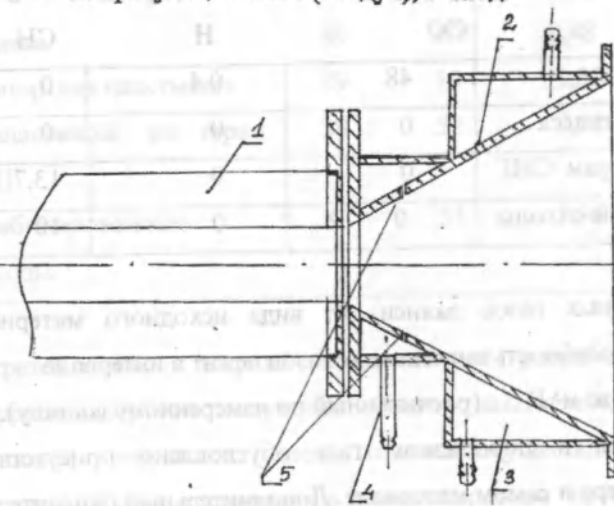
Конструкция насадка: 1-плазматрон; 2-расширяющийся насадок; 3-водяное охлаждение; 4-вход для спутного газа; 5-отверстия для подачи спутного газа в насадок.
